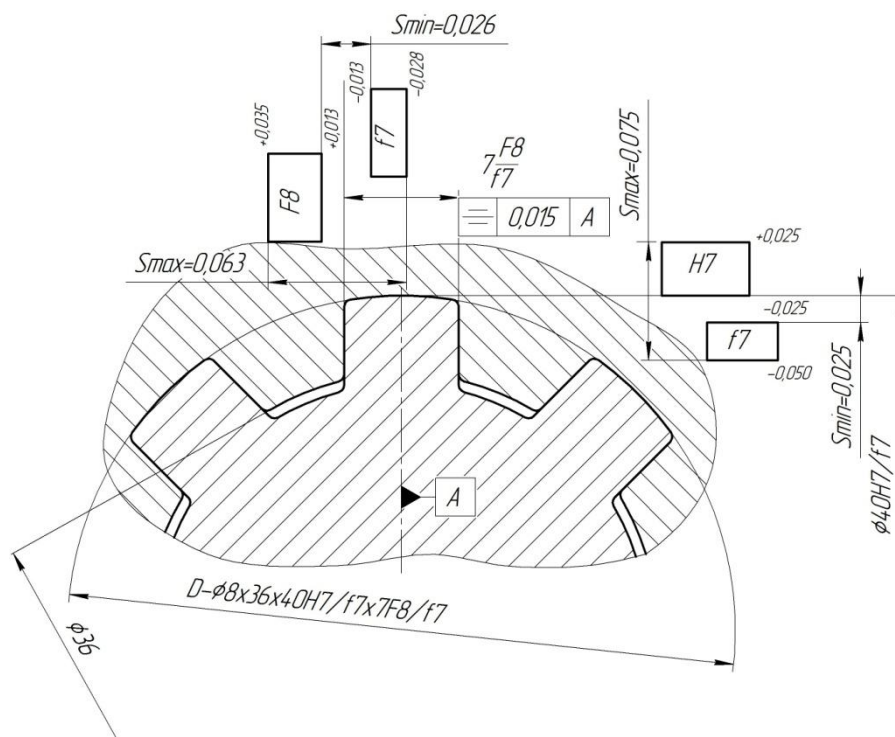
Схема расположения полей допусков в шлицевом соединении
